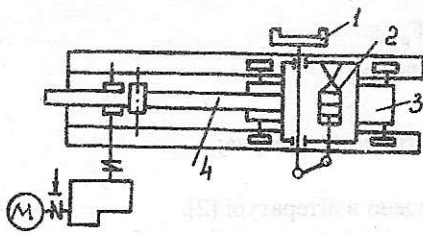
Схема штовхача поїздів візків з виливницями: 1-захват; 2-циліндр; 3-каретка; 4-рейка
